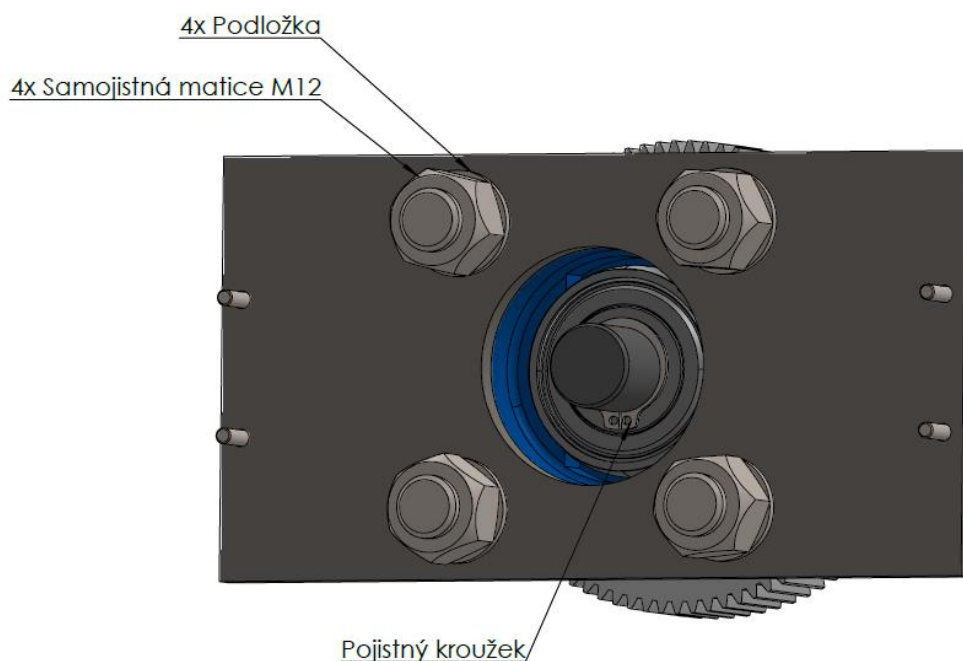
Schematické zobrazení uložení spoluzabírajícího kola
